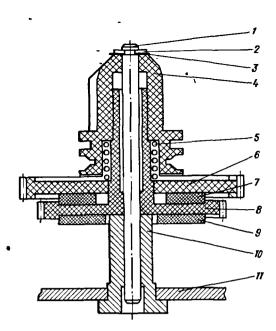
Шпиндель приемного узла: 1— ось; 2— фиксирующая шайба; 3— фторопластовая прокладка; 4— головка приемного узла; 5— пружнна; 6— зубчатое колесо приемного узла; 7— фрикционная шайба; 8— зубчатое колесо; 9— печатная шлата датчнка системы автостопа; 10— втулка; 11— шасси
